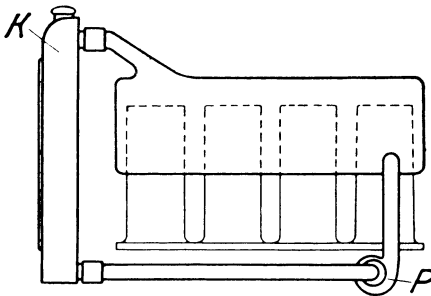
Vierzylinder mit Wasserkühlung und Umlaufpumpe. *K* Kühler, *P* Pumpe. Die vier Zylinder stecken mit ihren Köpfen im Wassermantel
